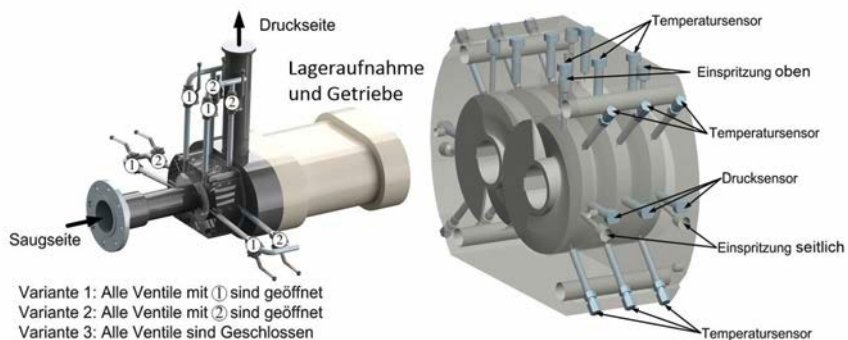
3D-Ansicht des Casing Gas Kompressors mit Kennzeichnung der Einspritzpositionen (links) und 3D-Ansicht des Gehäuses inklusive eingebauter Messtechnik (rechts).
